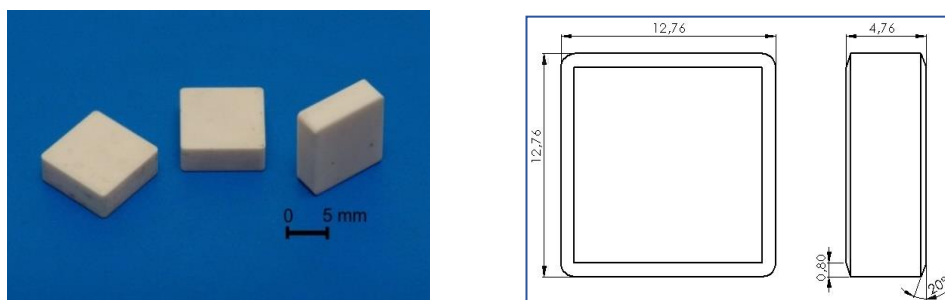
a) Ferramenta de alumina; b) Desenho esquemático das dimensões da ferramenta.
